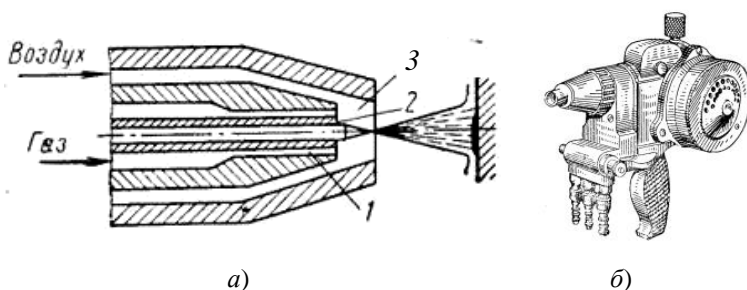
Схема установки газовой металлизации (а) и газовый металлизатор (б): 1 – отверстие для смеси ацетилена с кислородом; 2 – частицы расплавленного металла; 3 – отверстие для сжатого воздуха
